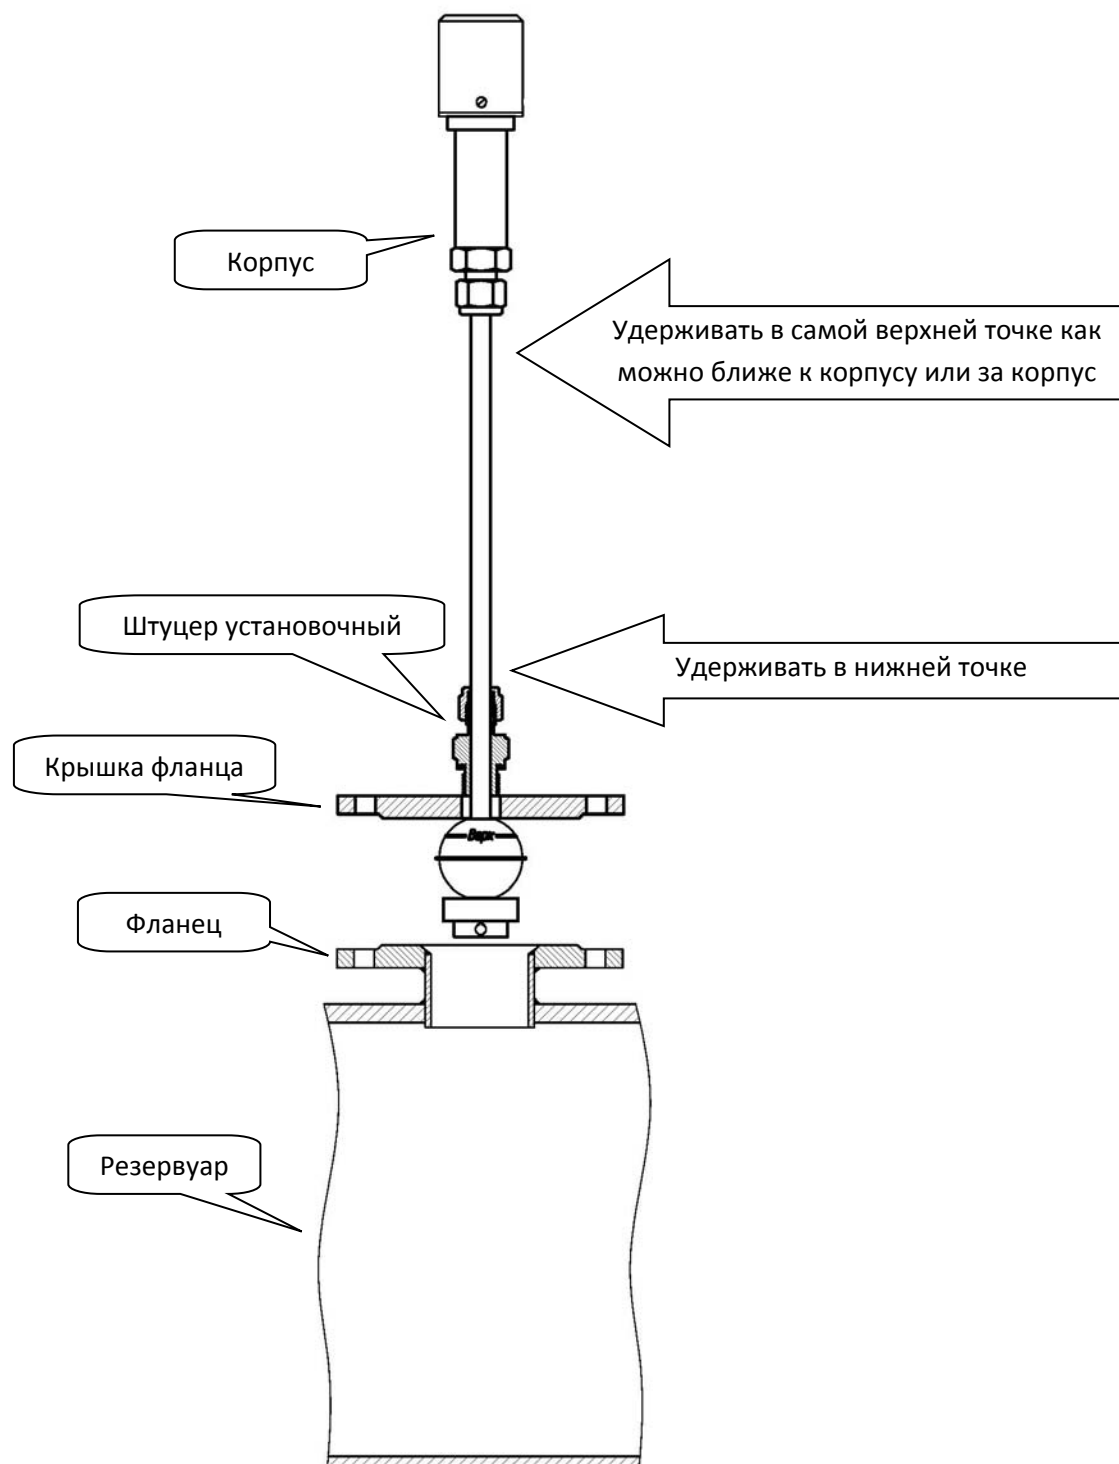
Правильное расположение и удерживание уровнемера над резервуаром с фланцем на патрубке
